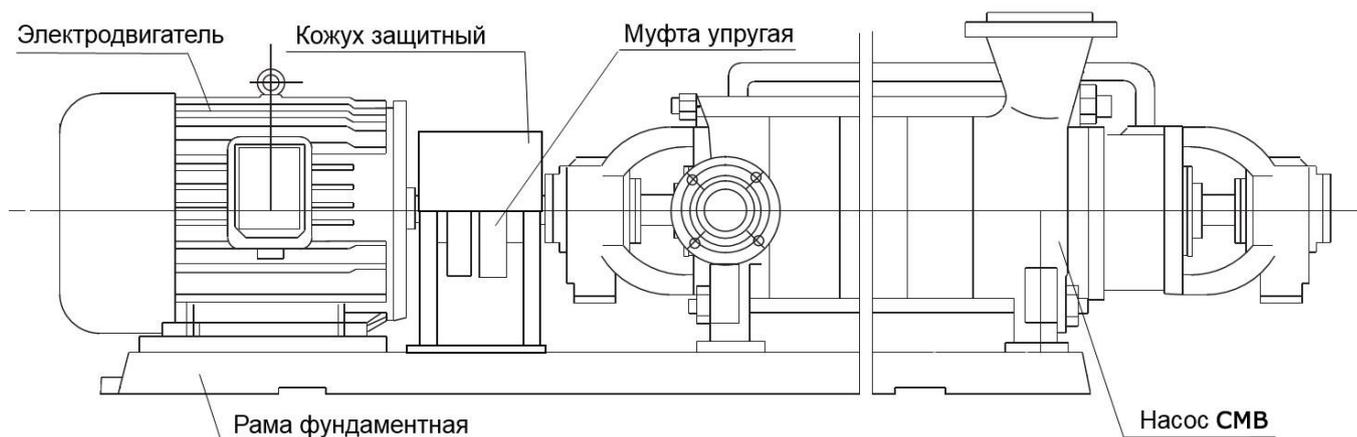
Сборочная схема агрегата на основе насоса CMB
